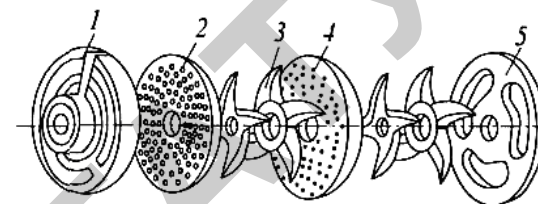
Режущий механизм волчка К7-ФВП-160-2:
